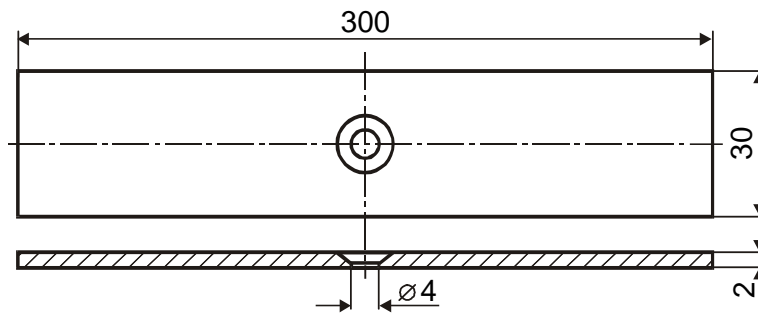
Конструкція зразка пластини із зенкованим отвором
